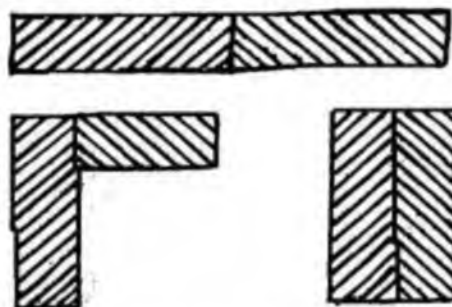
Рекомендуемые типы сварных соединений
